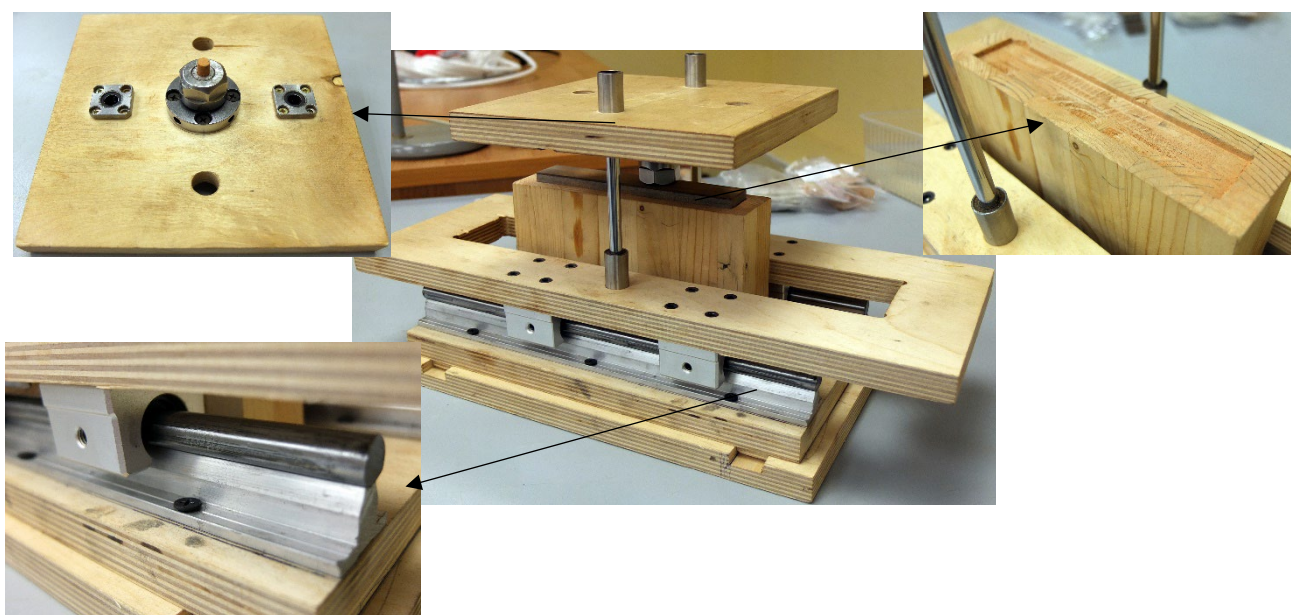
Приспособление для калибровки и шлифовки образцов
